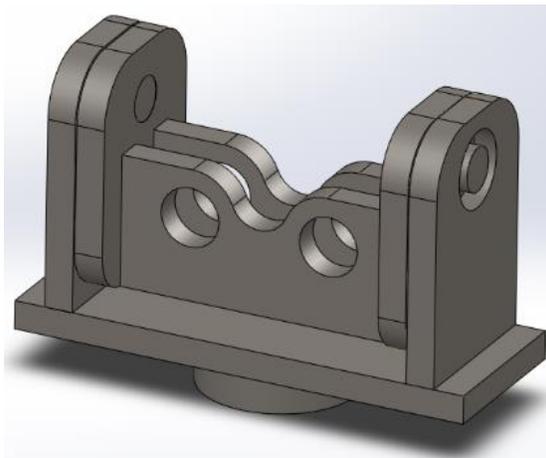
Placa porta rodamientos sostenedores (Pieza N° 2 de ensamble). Fuente: Elaboración propia.
